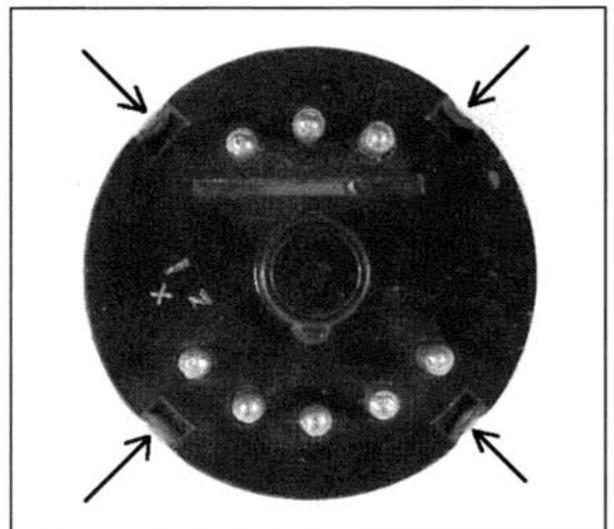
Befestigung der Sockelplatte einer Telefunken-Röhre, alte (große) Bauform.
